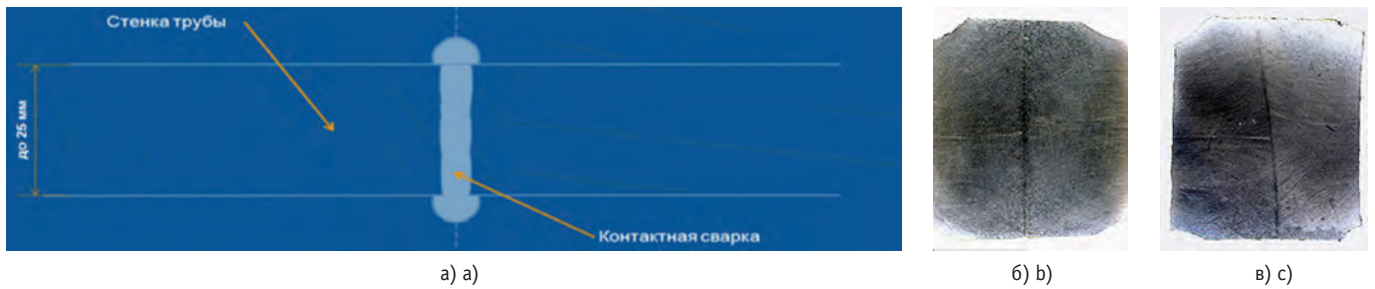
Сварное соединение, выполненное КСО: а) схема соединения; б) и в) макрошлифы, содержащие зону сплавления без смещения кромок (б), со смещением кромок (в)
